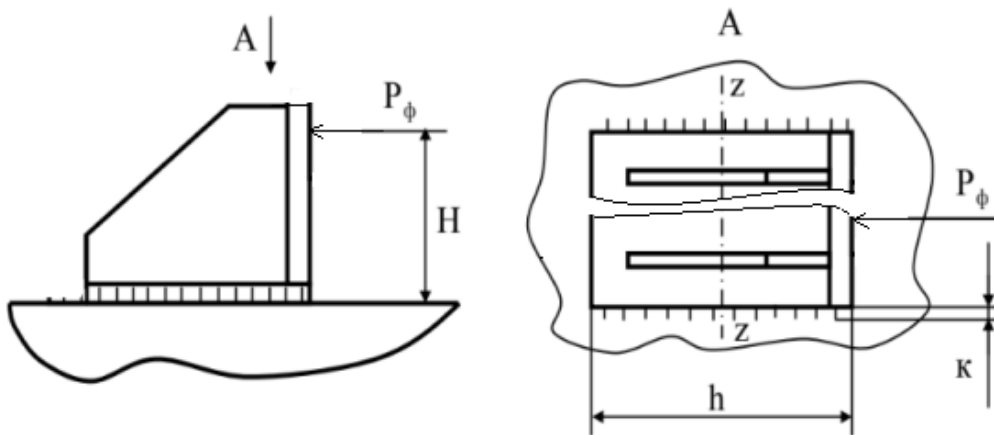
Розрахункова схема закріплення упора зварними швами
